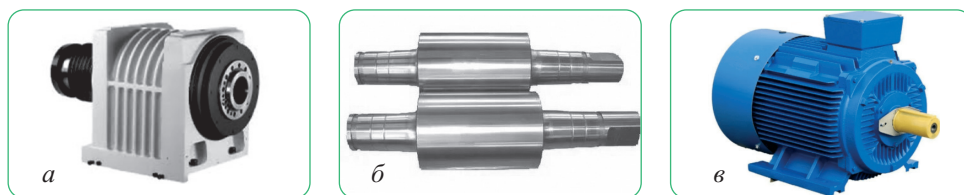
а – шпиндель токарного станка; б – валки в прокатном стане; в – электродвигатель
